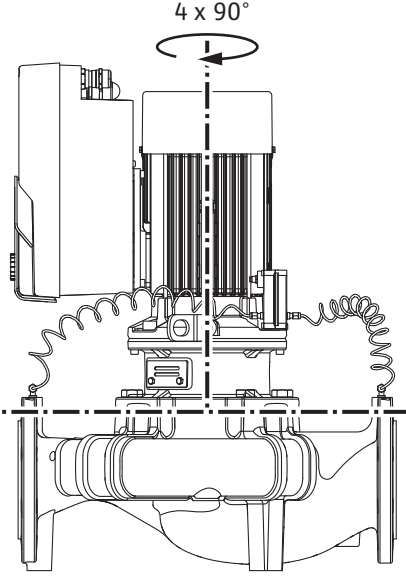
Dikey motor mili ile izin verilen montaj konumları
